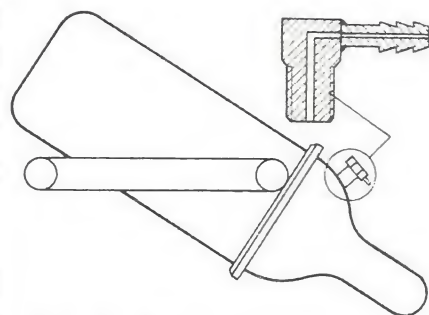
Штуцер, изготовленный из пробки-заглушки.
